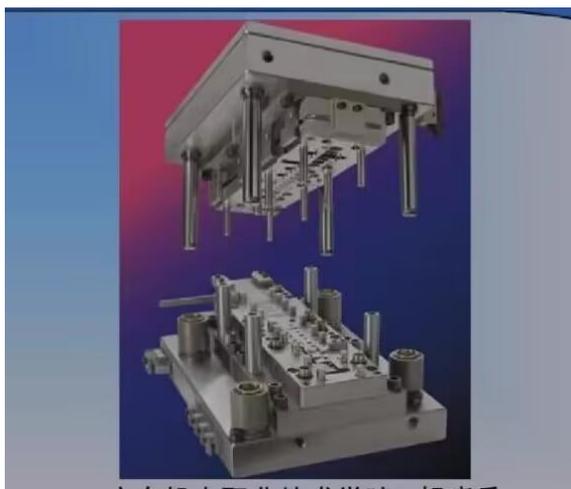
Вид штампа для листовой обработки (в разборе)
